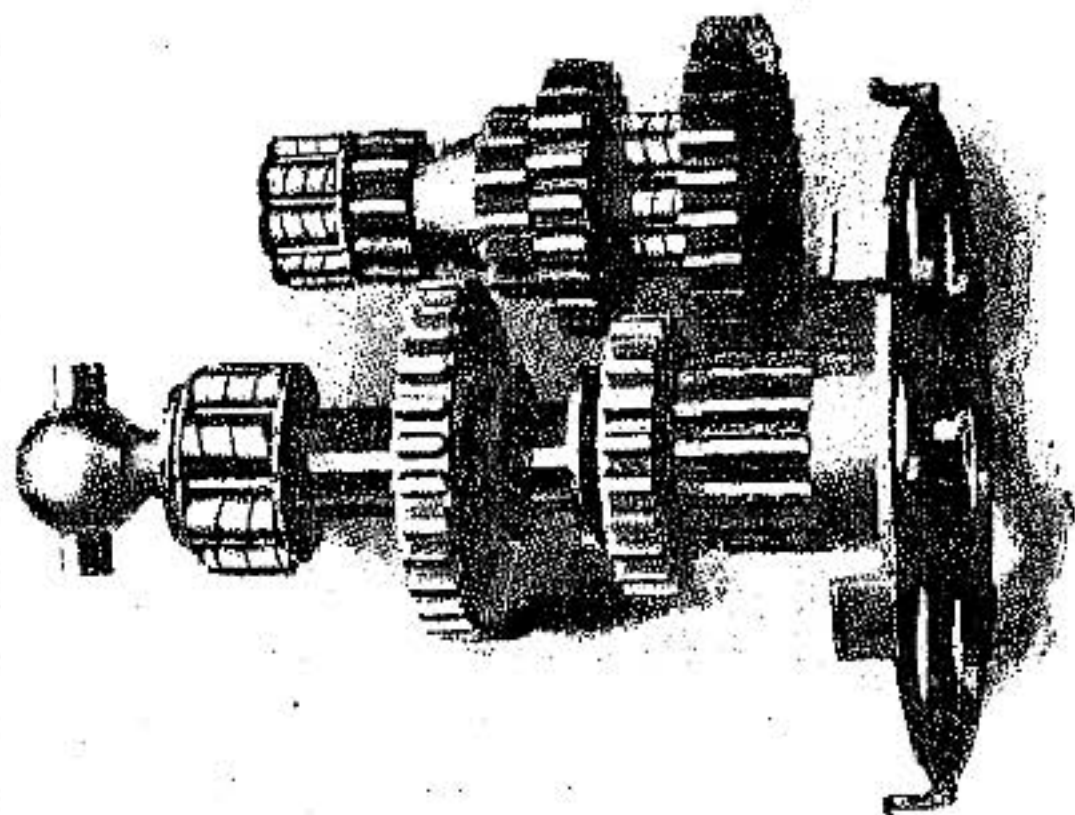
Зубчатки коробки скоростей Гупмобиля.
